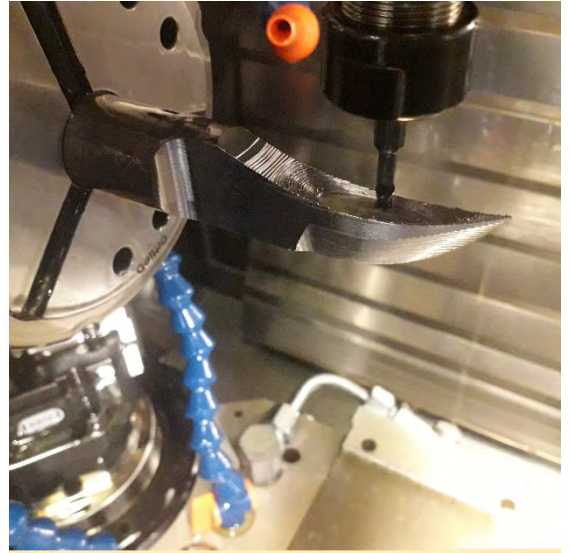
Получистовое фрезерование внутренней линейчатой поверхности детали сферической фрезой $\varnothing 4$ мм ($r = 2$ мм)
